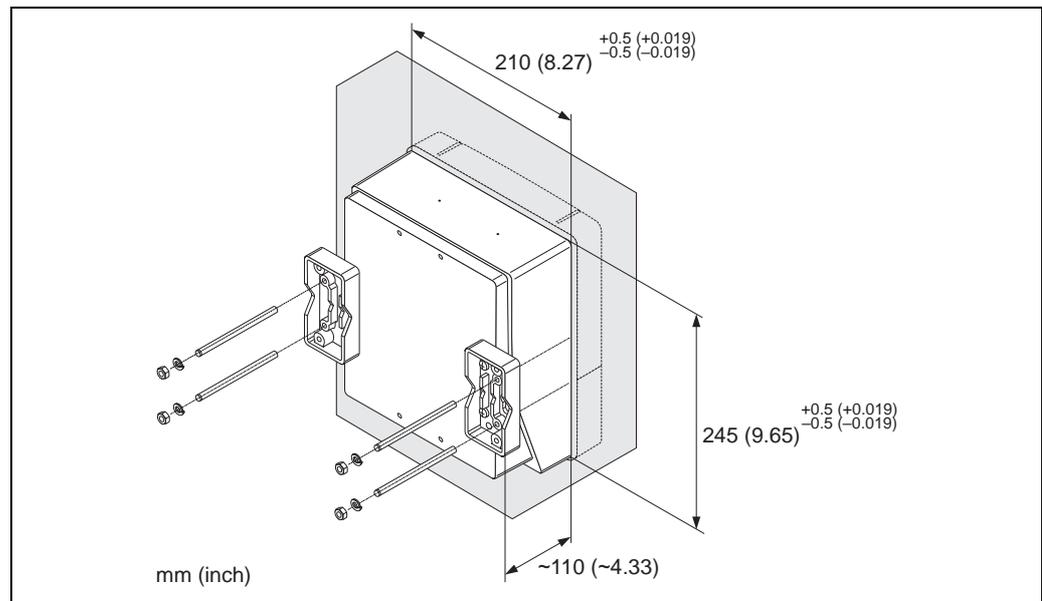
Schalttafeleinbau (Wandaufbaugeschäuse)
